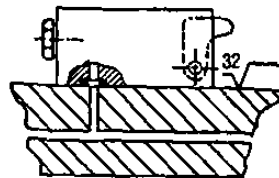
El montaje de partes con empaques o-rin requiere de un ajuste entre superficies de 32 milésimas de pulgada.
